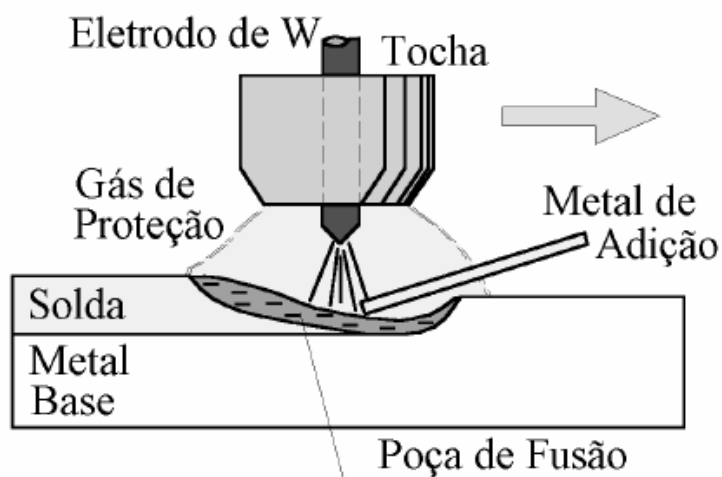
Soldagem TIG (Abrão, 2007)
